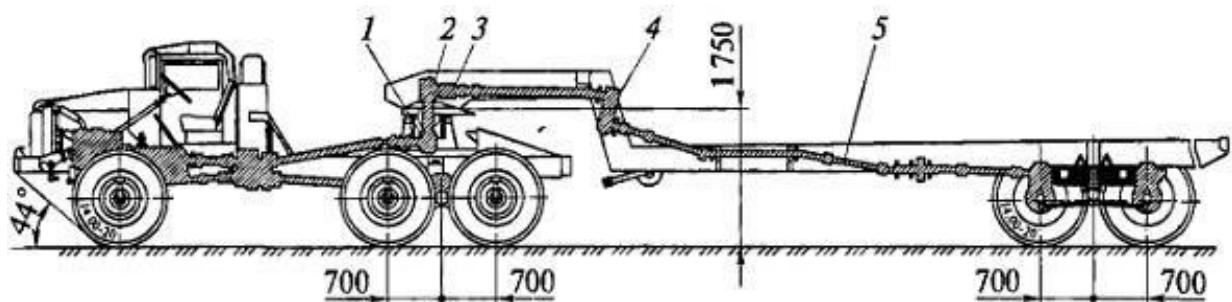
Схема розташування агрегатів механічного приводу осей напівпричепи.
